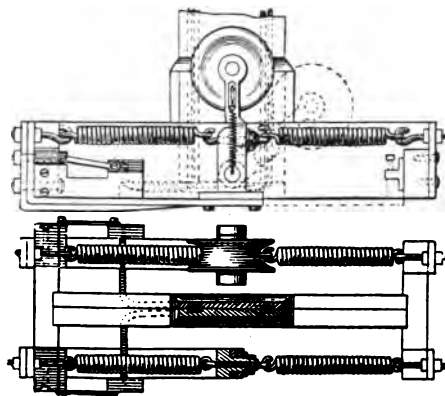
Caniveau système Love. — Trolley; plan et élévation.
